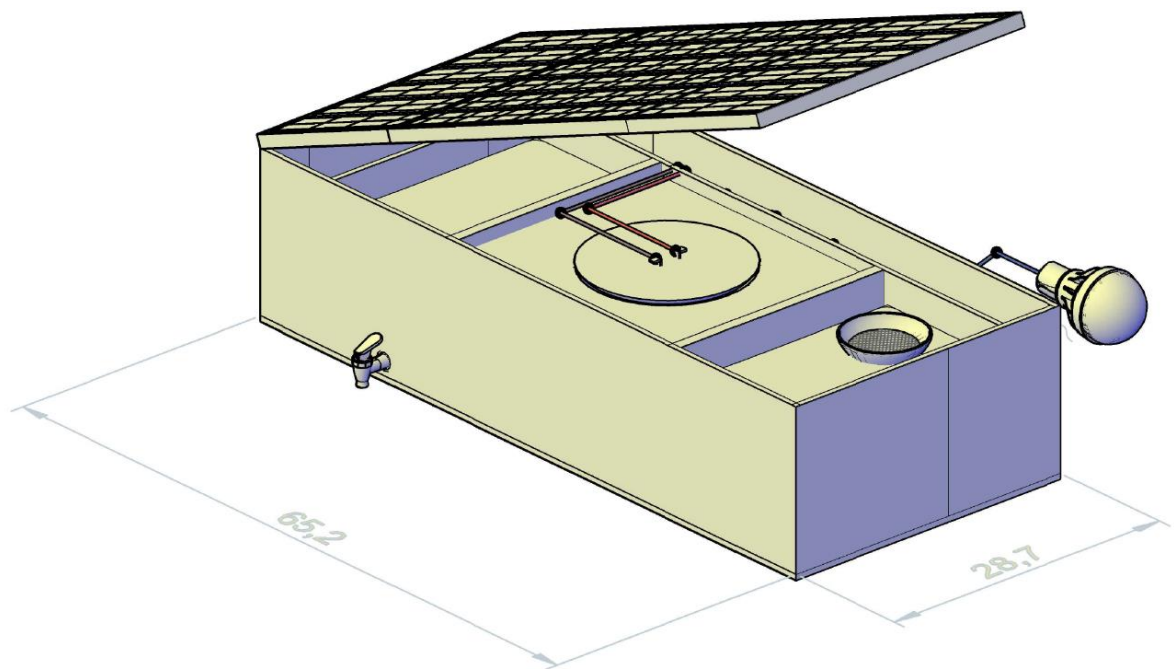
Dimensiones dispositivo de desinfección electroquímica vista isométrica
